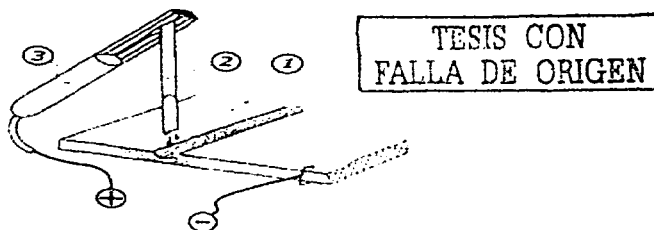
Soldadura por arco con electrodos metálicos [1].
